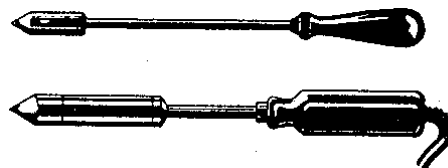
Ferros de soldar com bico de cobre e elétrico.
